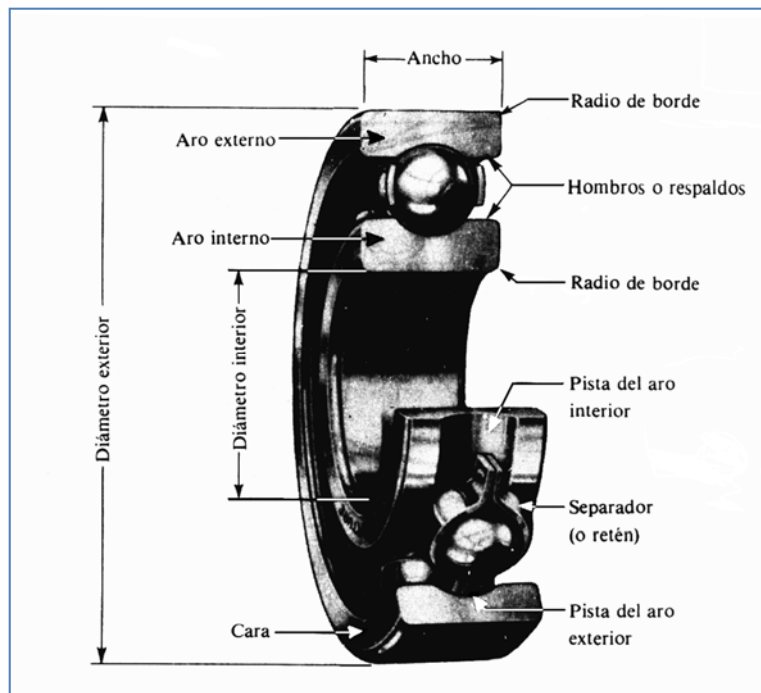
Rodamiento de bolas seccionado. [P2]
